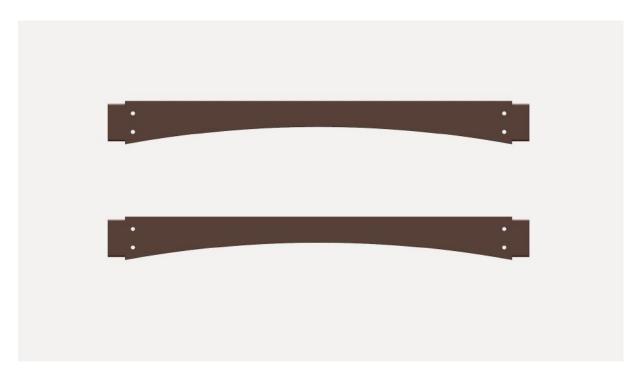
Detalhe - Furação das estruturas transversais do Pufe - Frontal e Posterior
